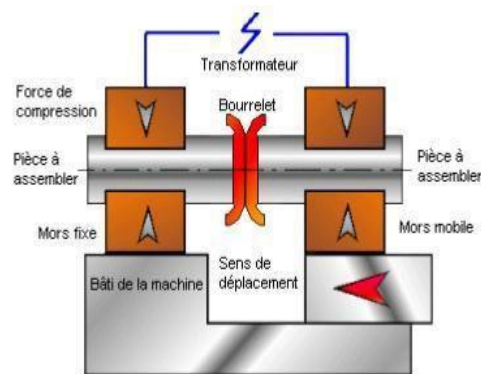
Soudage en bout par étincelage [8]
